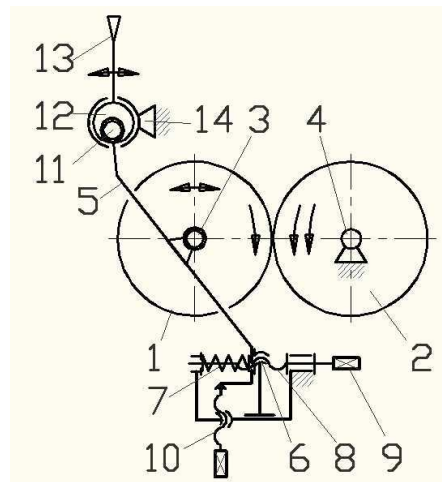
Схема установочного механизма с верхним расположением эксцентрикового вала
